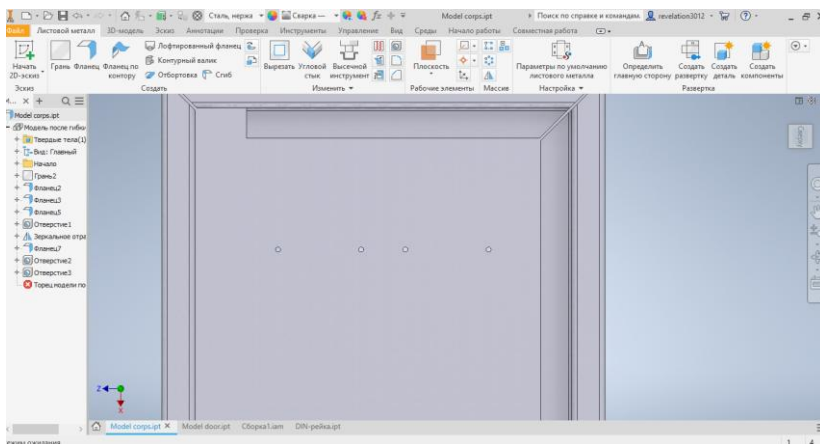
Отвори у монтажній частині корпусу щита для болтового з'єднання
